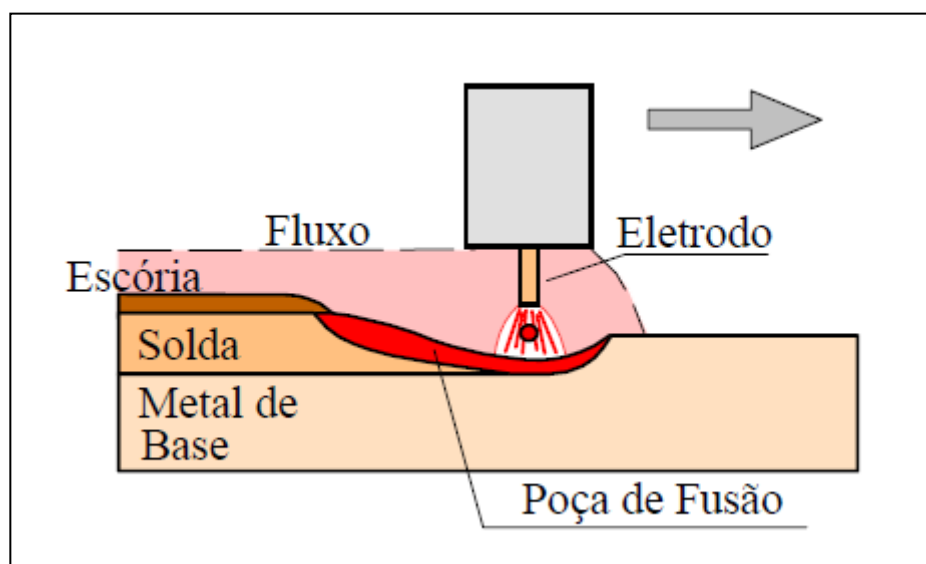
Esquema de Suberged Arc Welding – SAW (Modenesi e Marques – Soldagem I - 2006)
